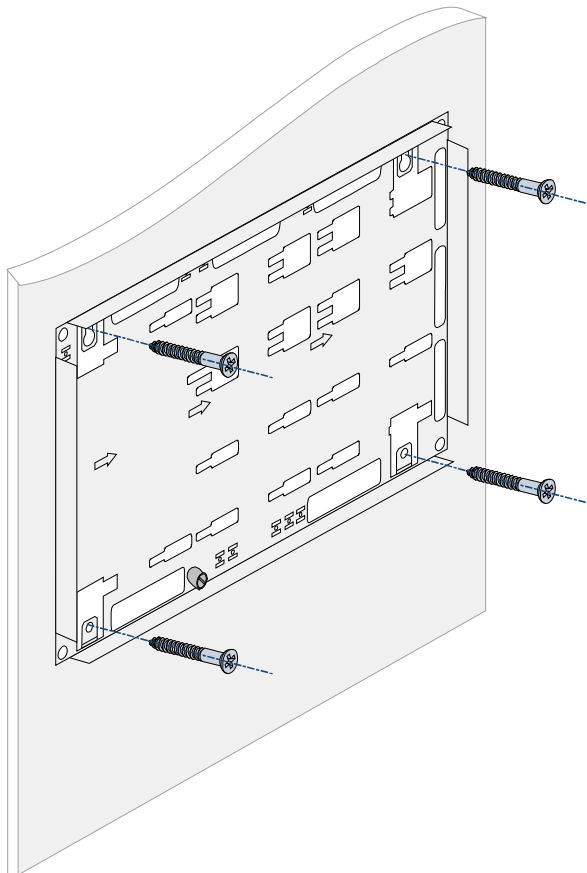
Fastgøring på monteringsoverfladen (eksempel med bagvæg til vandret opstilling)
